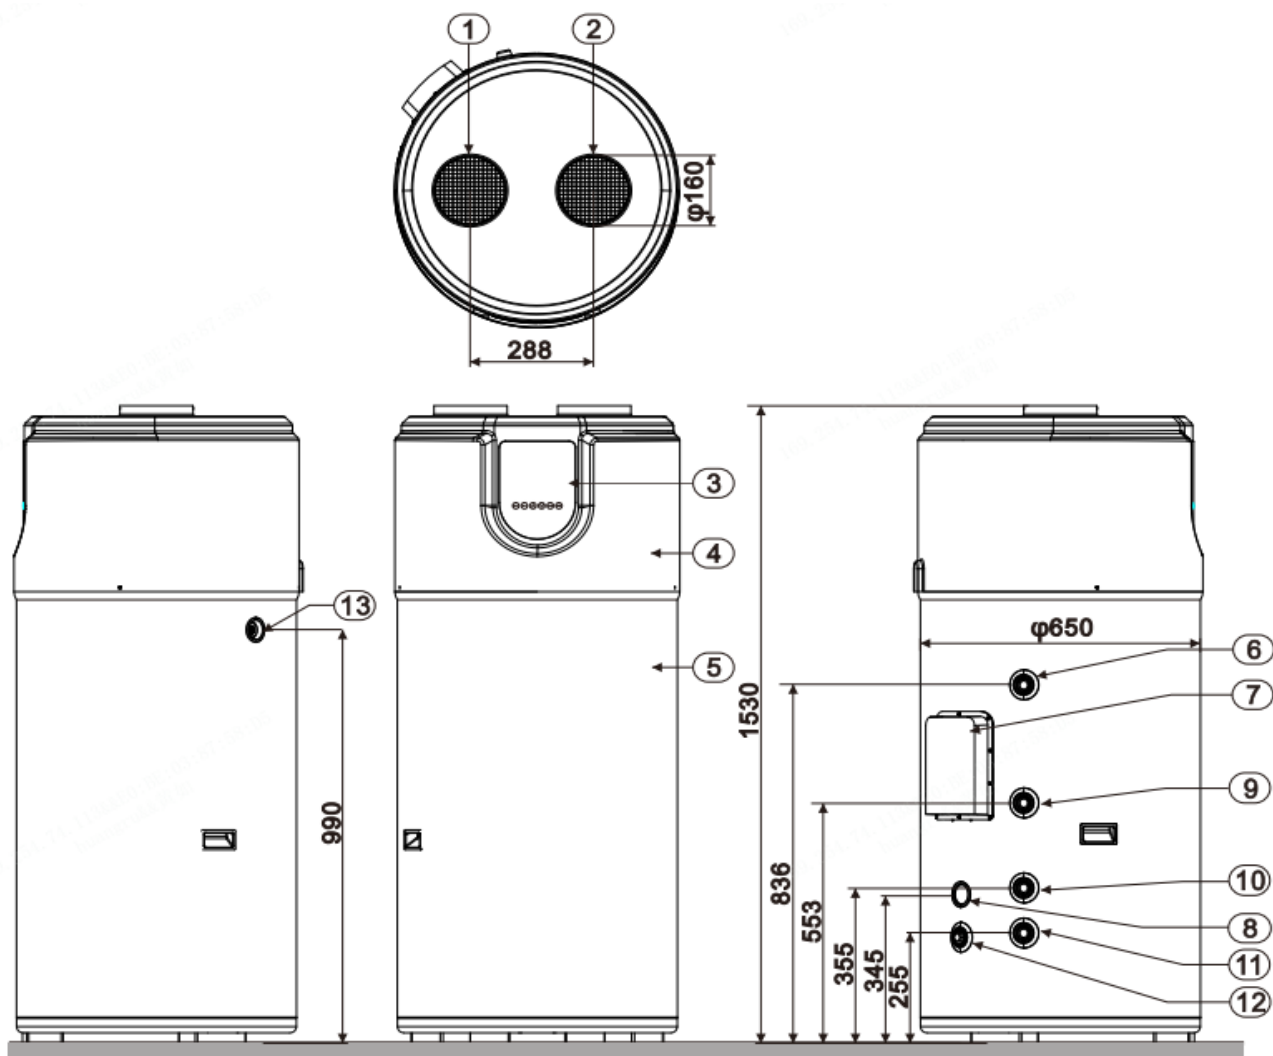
Zeichnung und Abmessungen des Geräts
